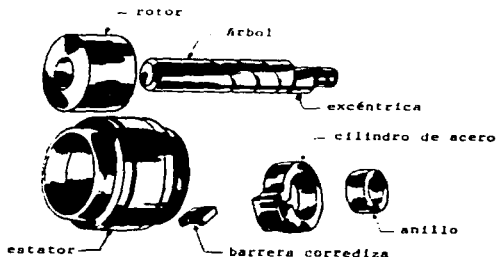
Partes de un compresor rotatorio de pistón rodante.
